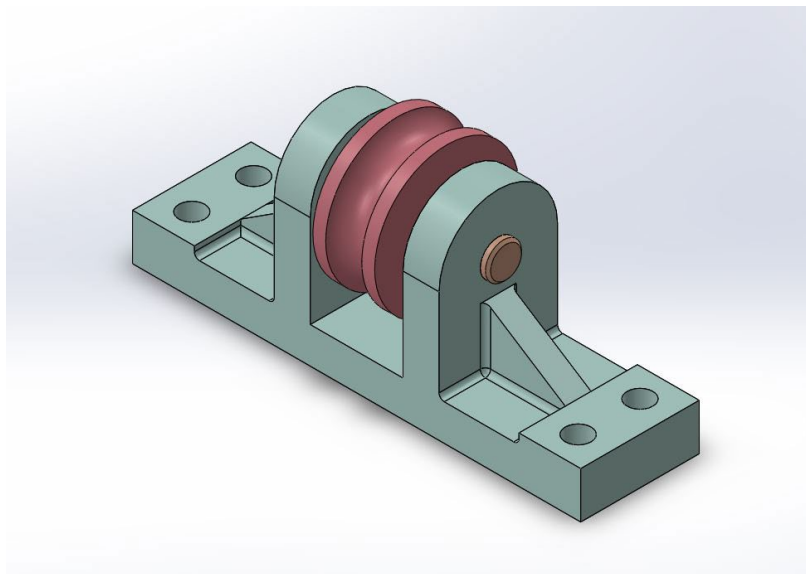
Твердотіла збірна модель Тримач кабелю у SolidWorks.
